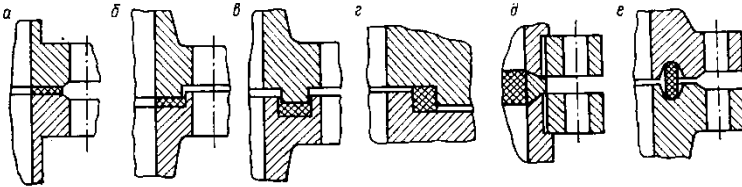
Виды поверхностей уплотнения фланцевых соединений: а – плоская; б – выступ-впадина; в – "шип-паз"; г – "в замок"; д – коническая; е – овальная
